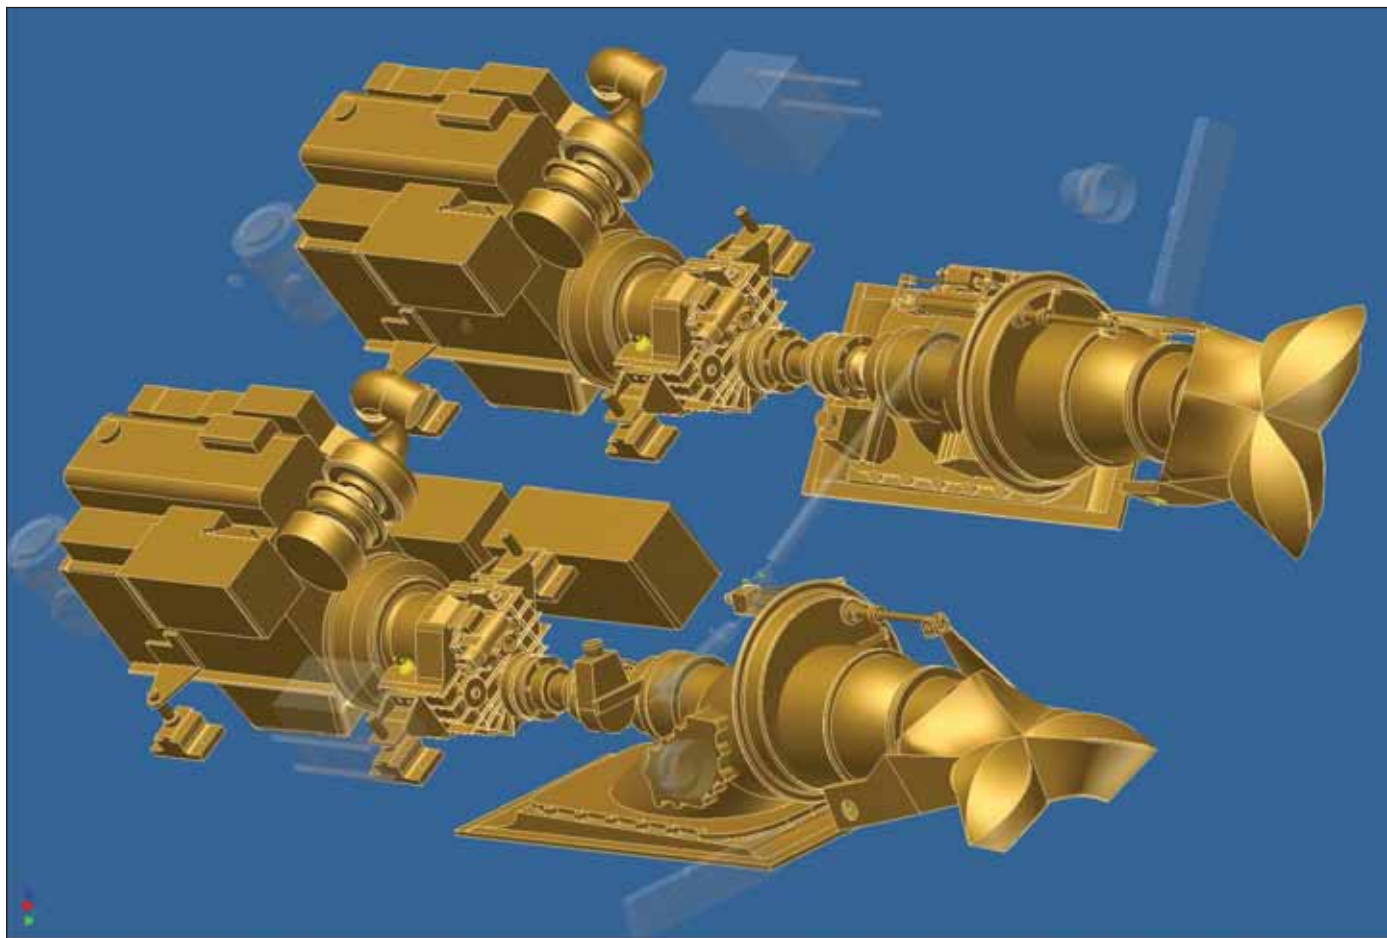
Стыковка ГД с водомером (перед размещением сборки в ЭЦМ катера)
